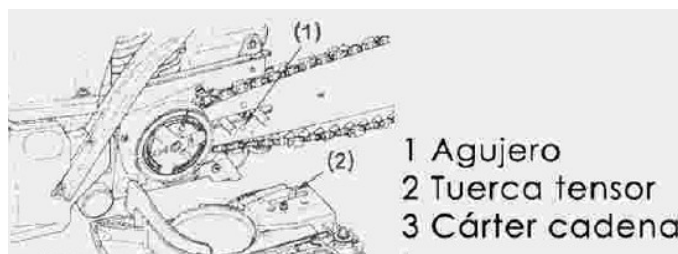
Montaje del cárter: 1, agujero; 2, tuerca del tensor; 3, cárter de la cadena
